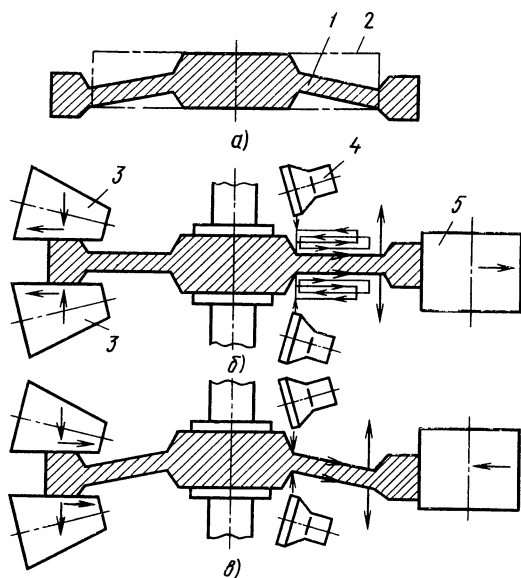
Схема процесса раскатки заготовок зубчатых колес:
